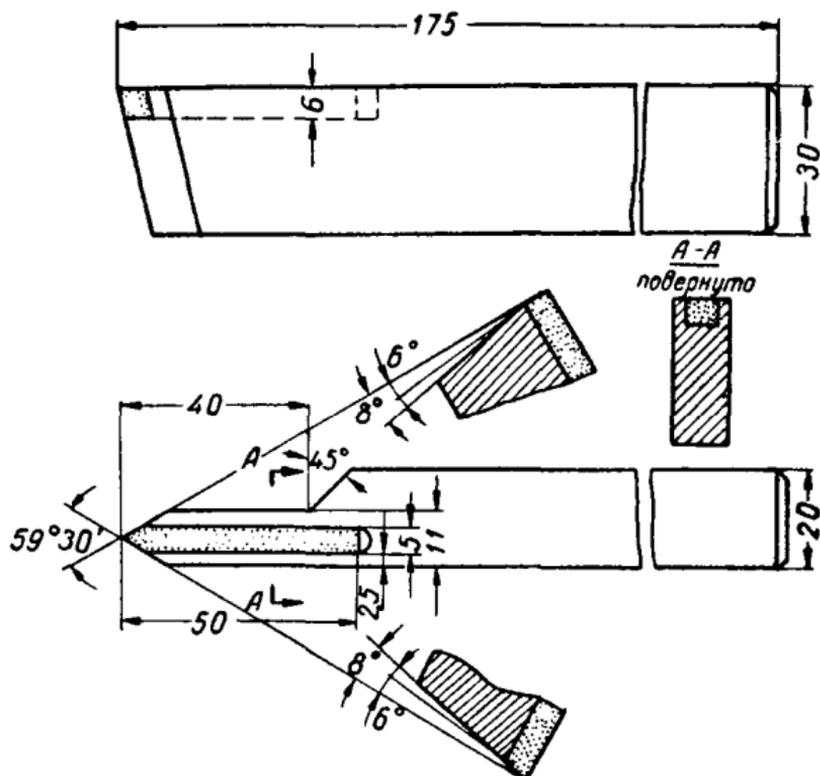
Резьбовой резец с плоской удлиненной твердосплавной пластинкой конструкции инж. П. С. Крыжановского.
